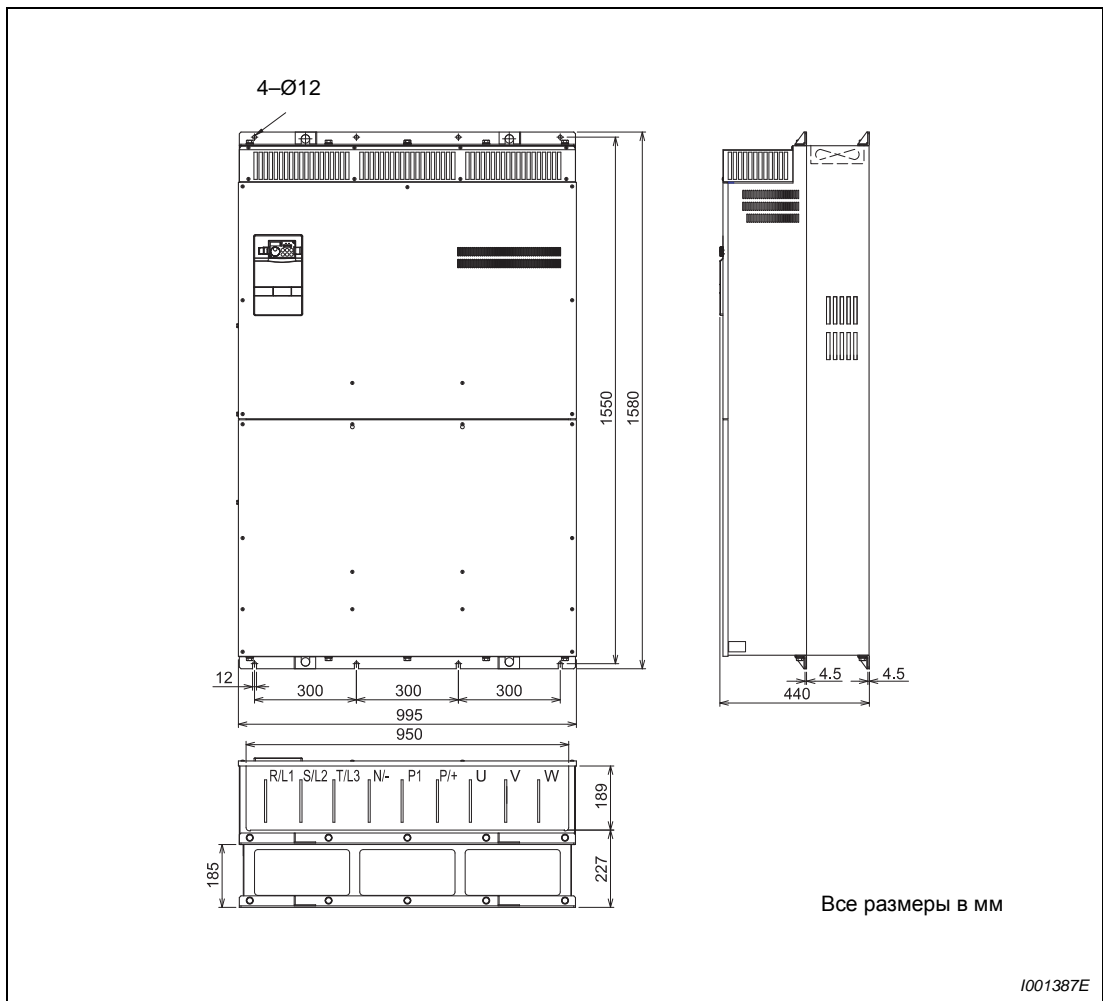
Размеры FR-F740-04320 и-06830
